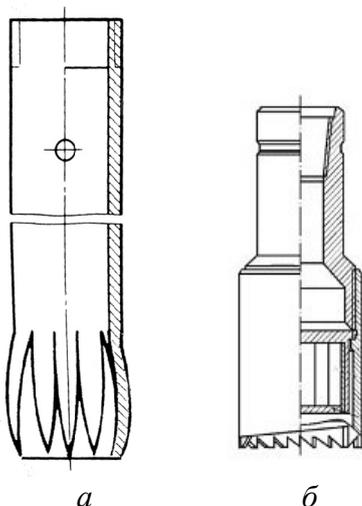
Схемы вспомогательных инструментов для очистки забоя от металла: а – трубный паук, б – магнитный фрезер-ловитель
